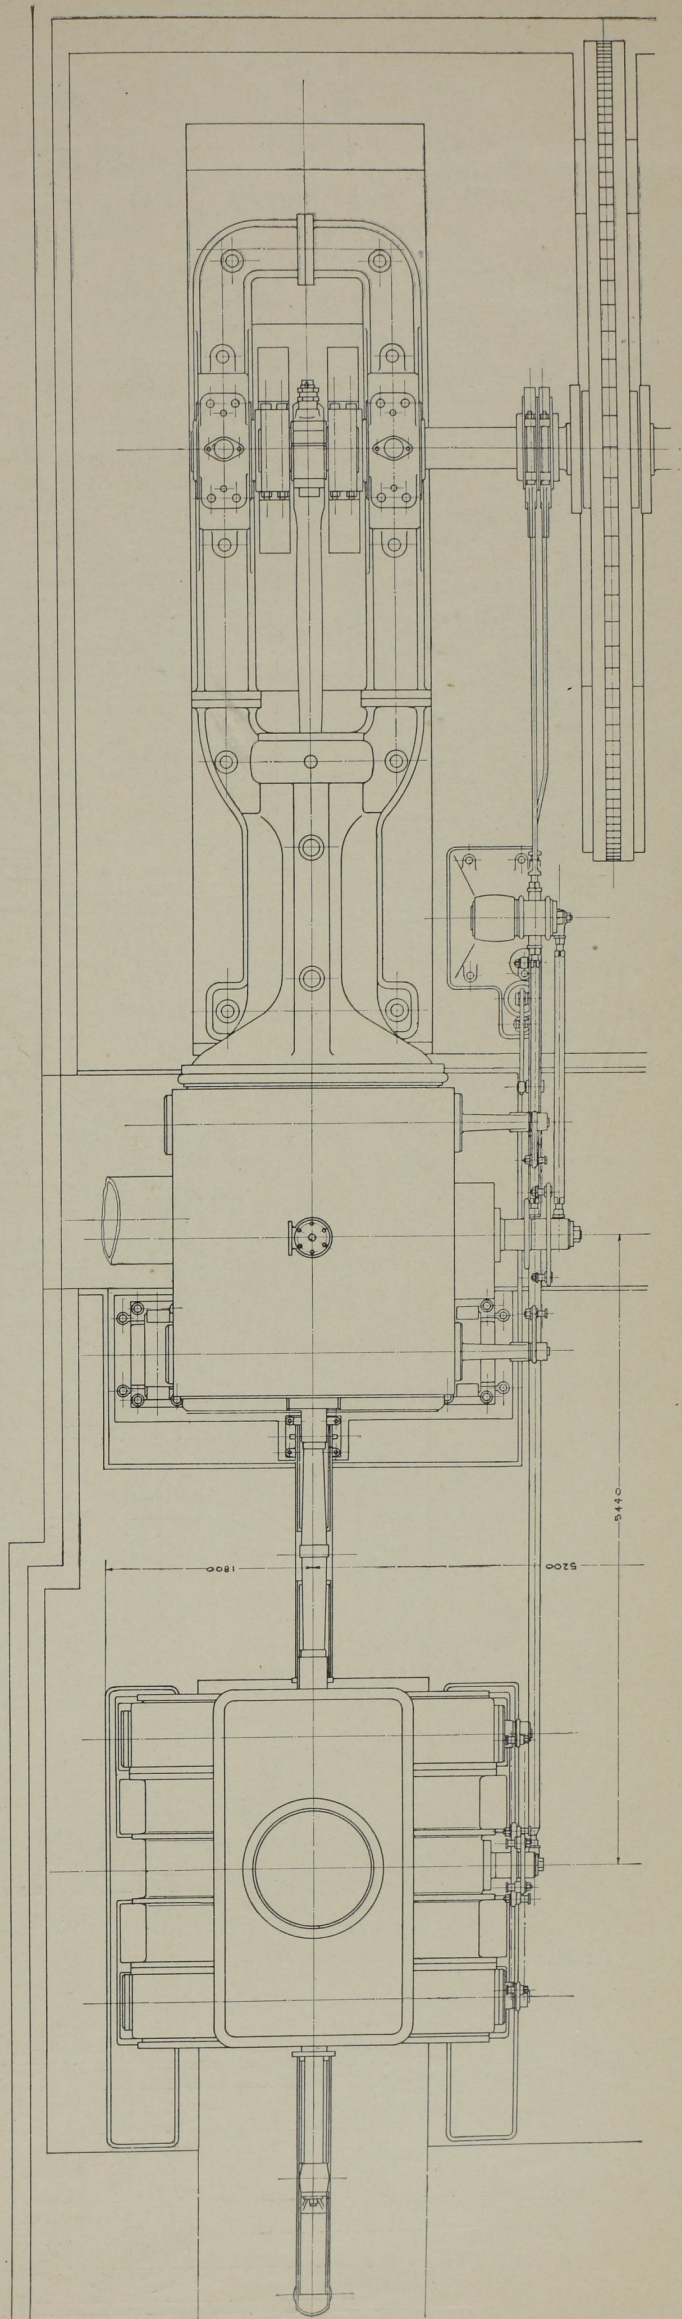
Grundriss der Niederdruckseite der Gebläsemaschine. Masst. 1 : 60.
